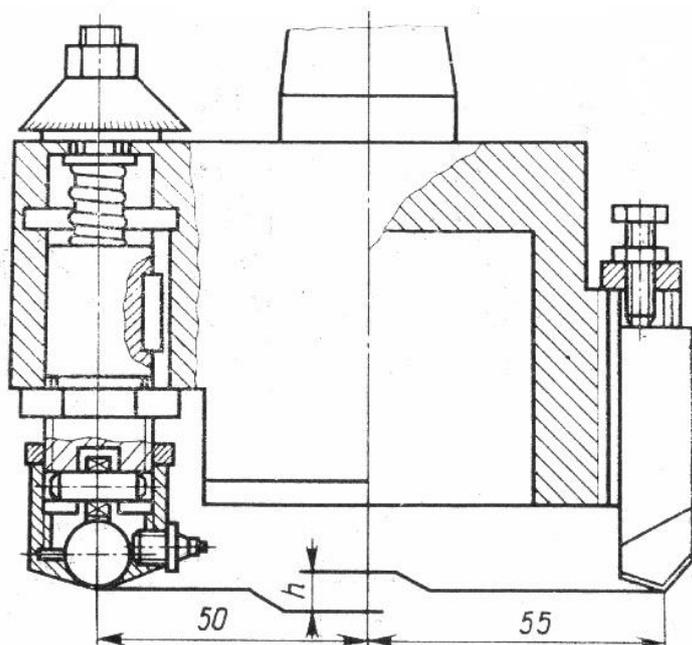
Инструмент для фрезерной обработки и поверхностного пластического деформирования
